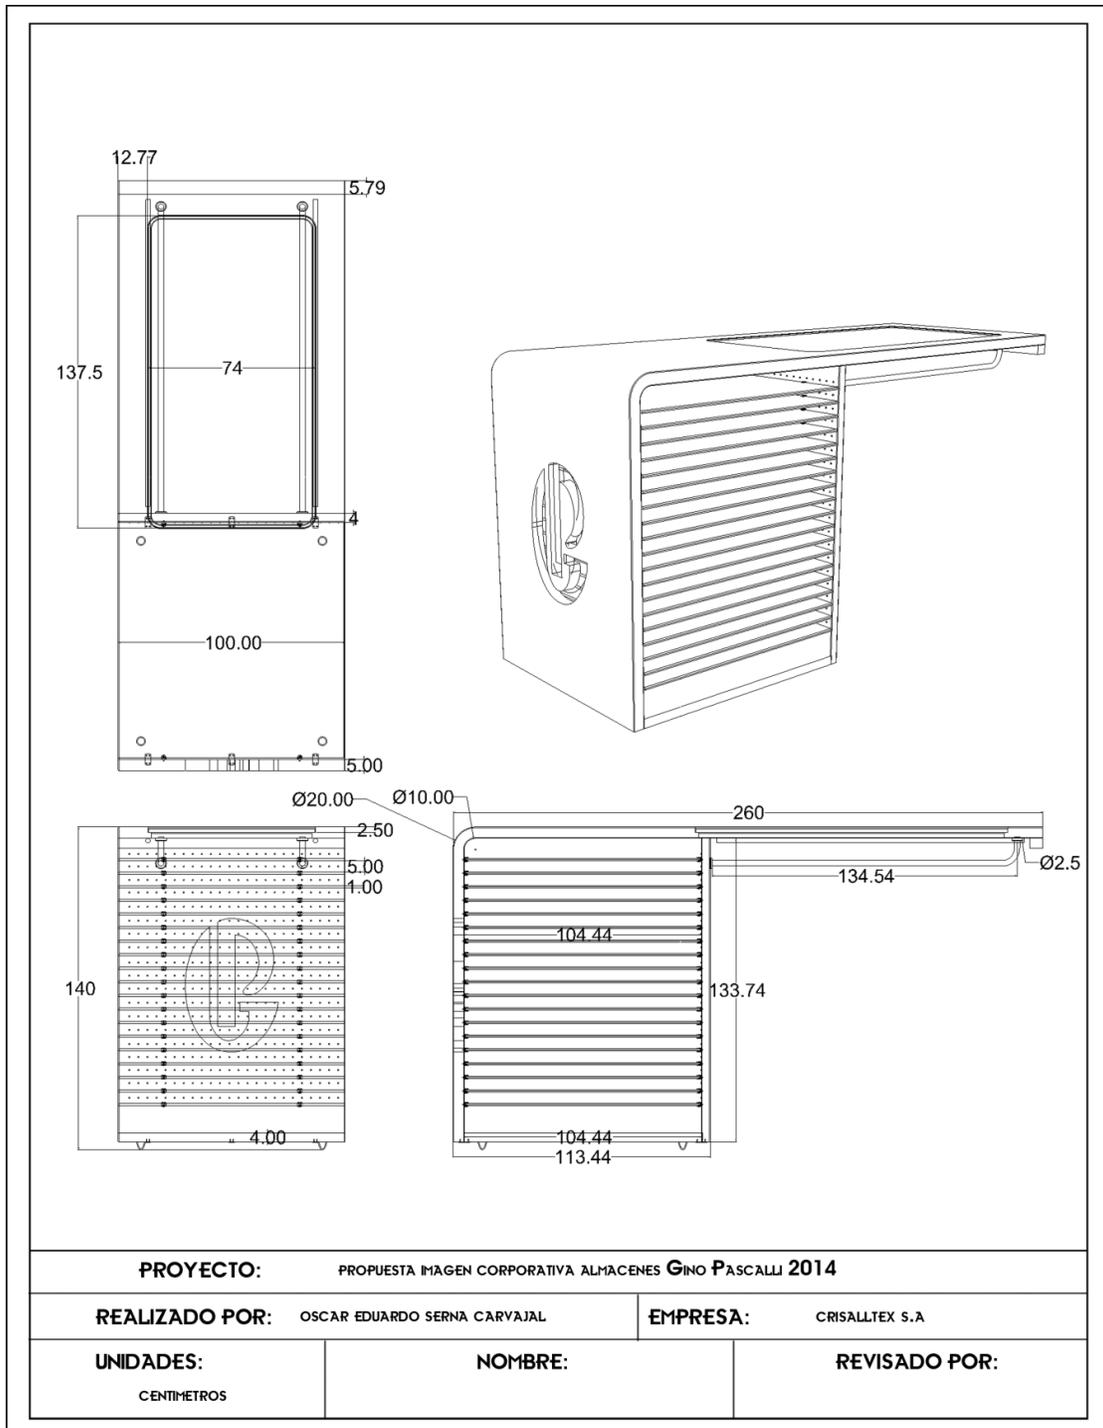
Planos Técnicos Exhibidor Fijo de Pared
